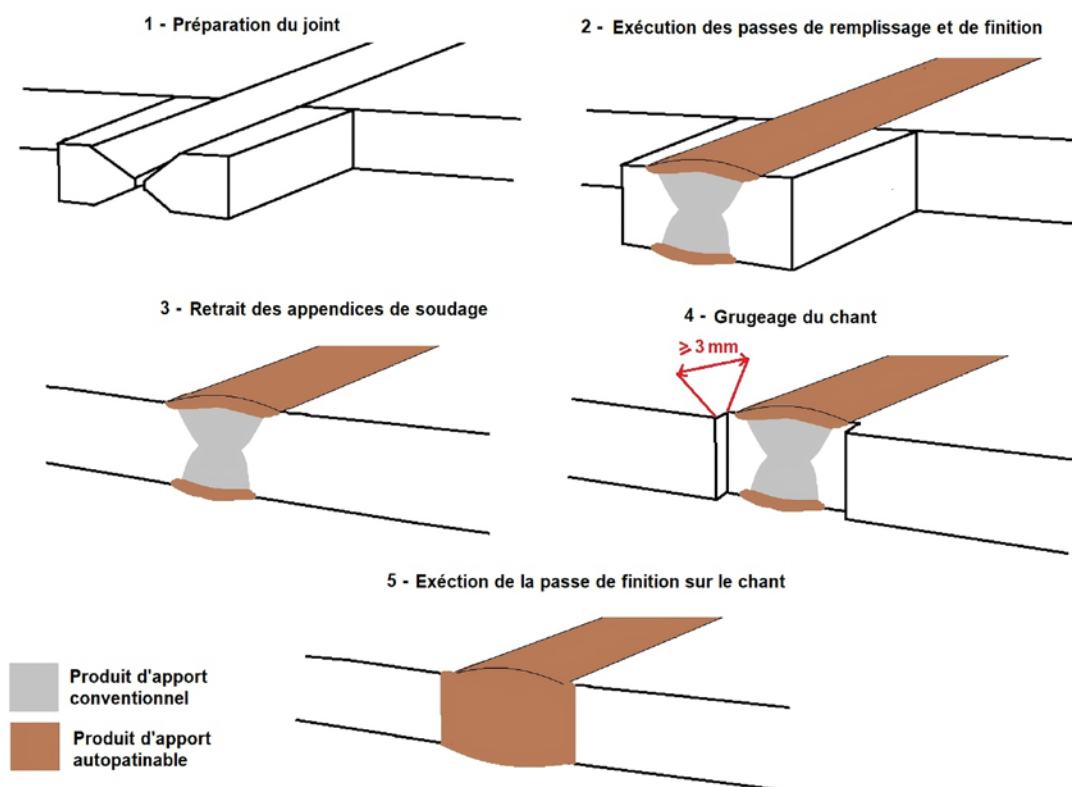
Étapes d'exécution d'une soudure bout à bout avec produit d'apport autopatinable utilisé seulement pour la passe de finition
